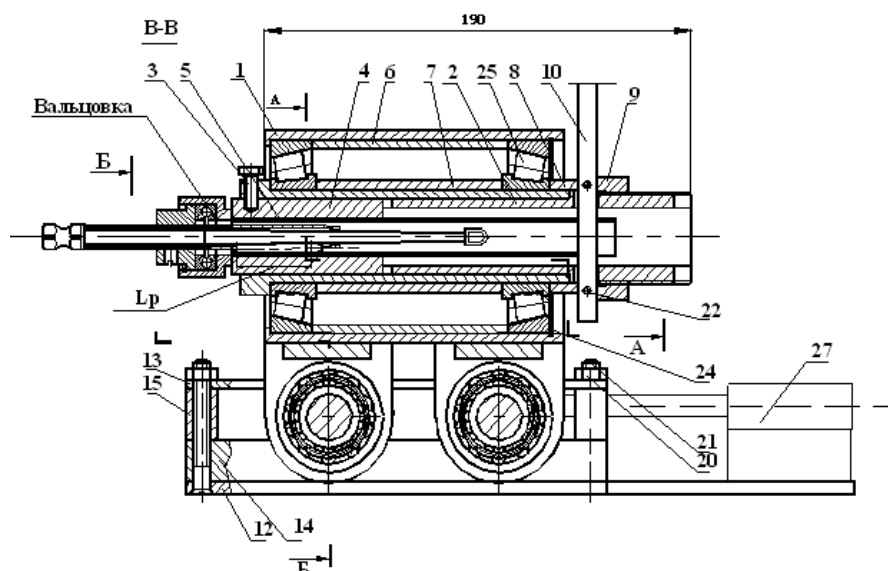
Узел крепления труб и втулки: 1-корпус; 2, 7-9- детали ротора; 3- испытываемая труба; 4- втулка; 10- рычаг; 12-15, 20,21- детали салазок; 22-24- крепеж; 25- подшипники; 27- датчик измерения осевого перемещения
